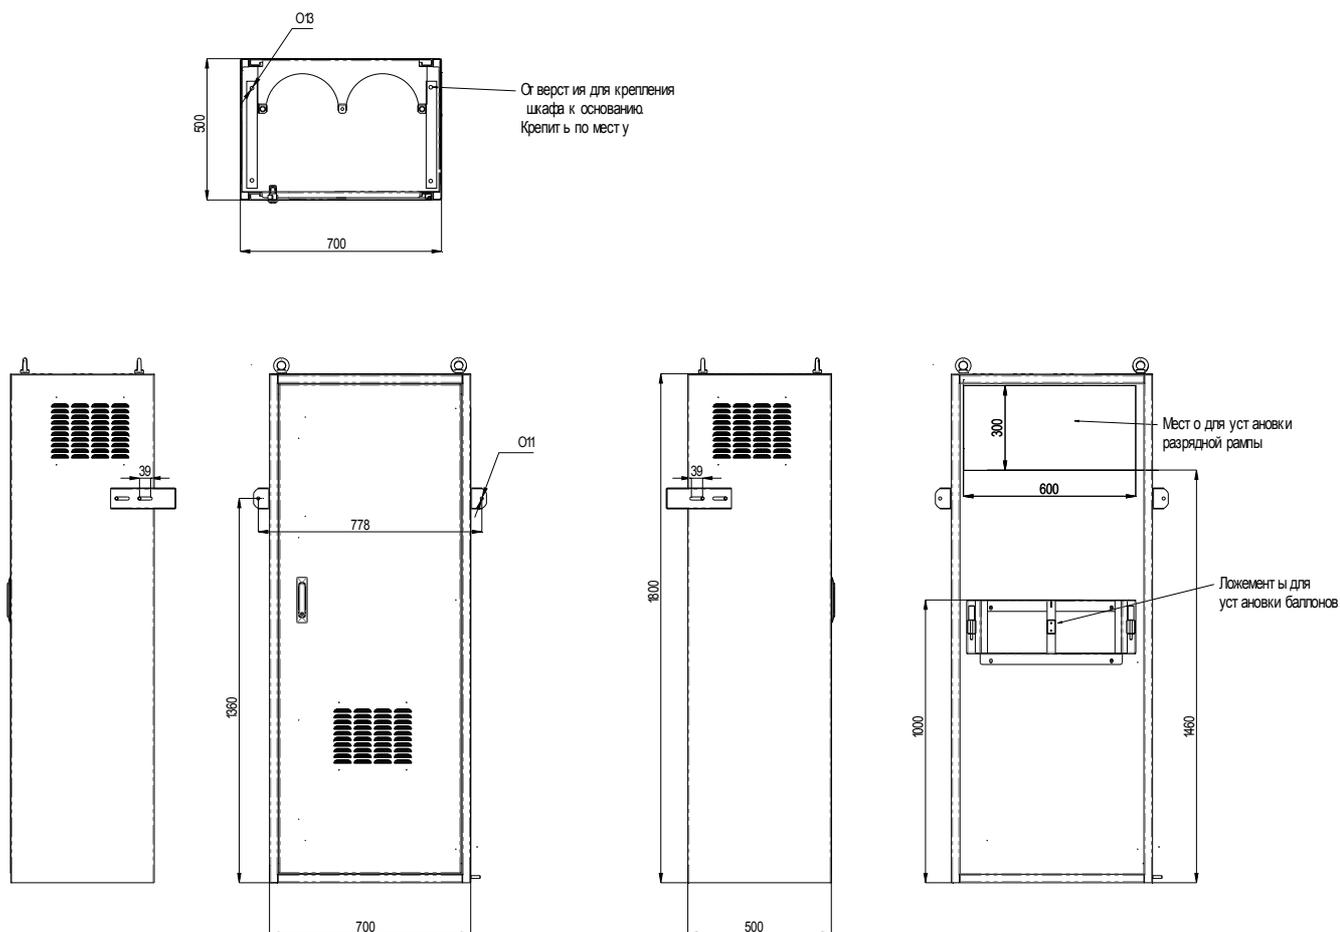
Габаритный чертеж шкафа 1875Н1
